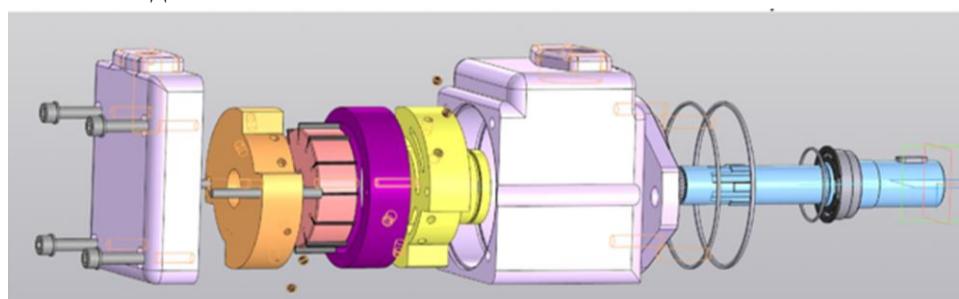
3D модель пластинчатого насоса Bosch PVV
